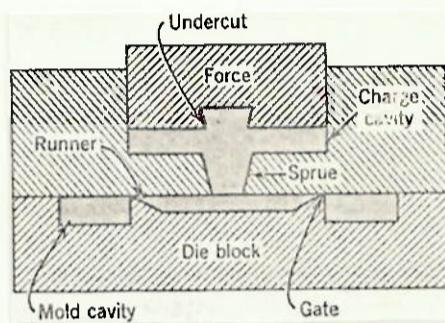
molde partido mostrando montante, canais, constrição e cavidade
